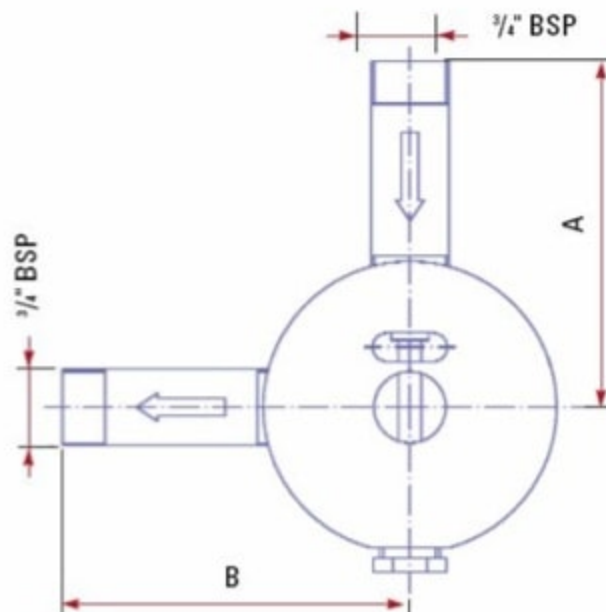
Дозаторы TP-50, 80 (новый тип), TP-50/20, 80/20 (старый тип) . Габаритные размеры изделий.
